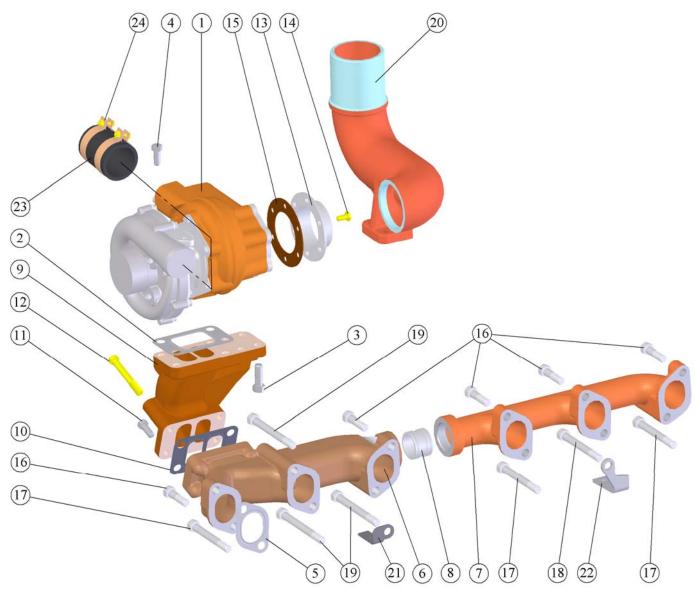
Система впуска и выпуска. Fig. 6 Engine intake and exhaust system.
